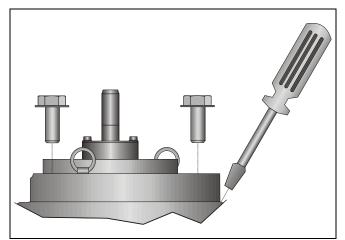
Desserrage et retrait des vis au niveau du couvercle de filtre
